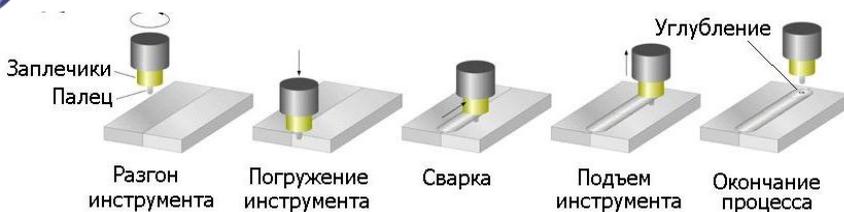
Этапы процесса сварки трением с перемешиванием.
